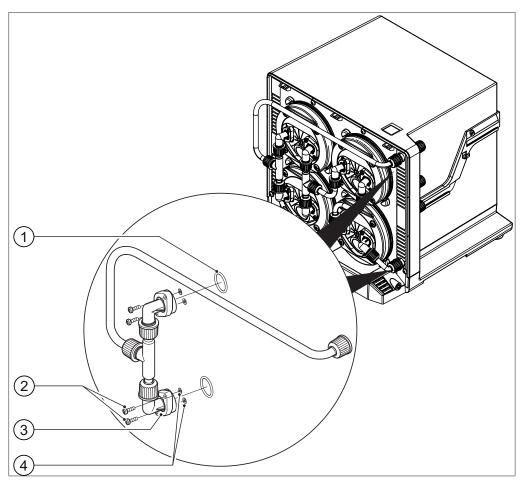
Componentes de unión, piezas de conexión y juntas tóricas de la V-600
